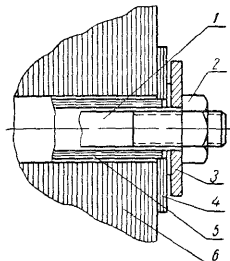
Прессовка стальных листов стержней стяжными шпильками:
